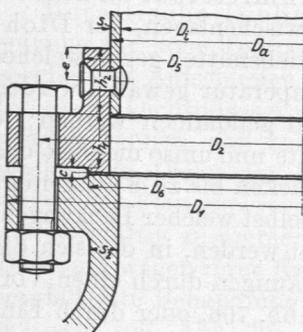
Flanschverbindung mit angenietetem Rohr.
